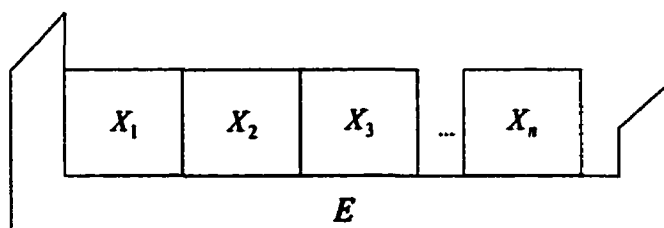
Exemple d'assemblage d'un cas linéaire
